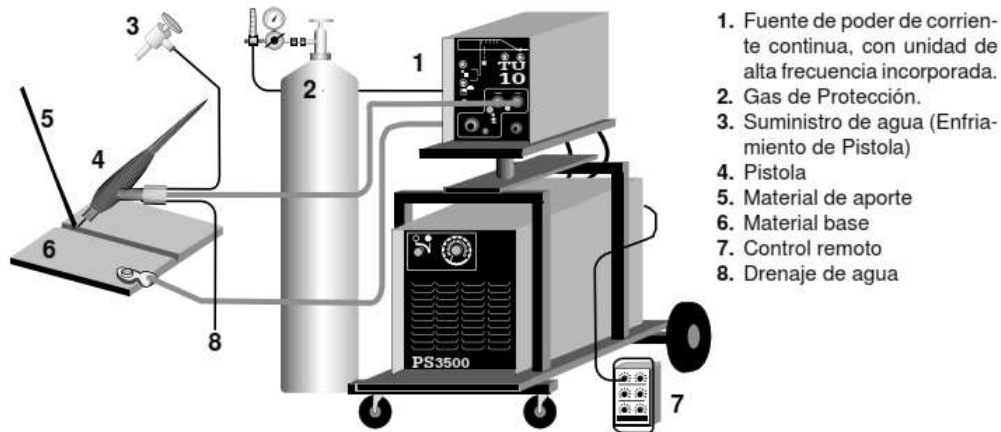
Diagrama esquemático del equipo básico utilizado en soldadura por el sistema TIG [29].
